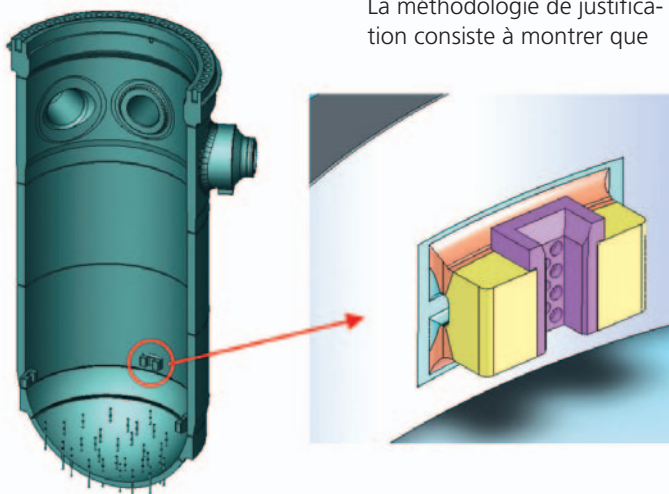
Vue d'ensemble des supports M du palier 900 MWe.
